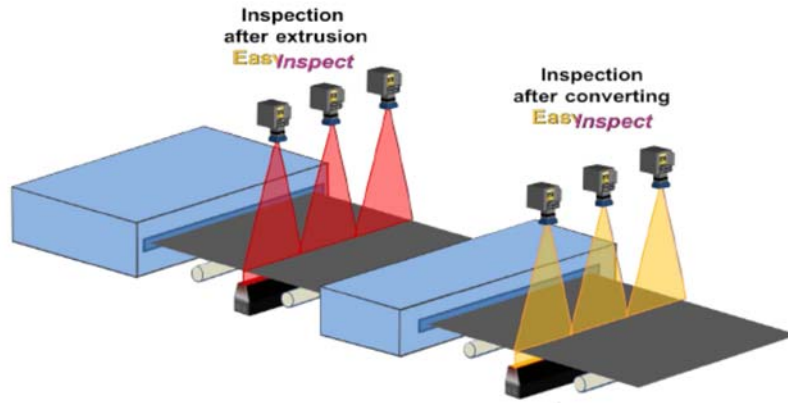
Esquema montaje de sensores de inspección en línea de extrusión de lámina/film.
